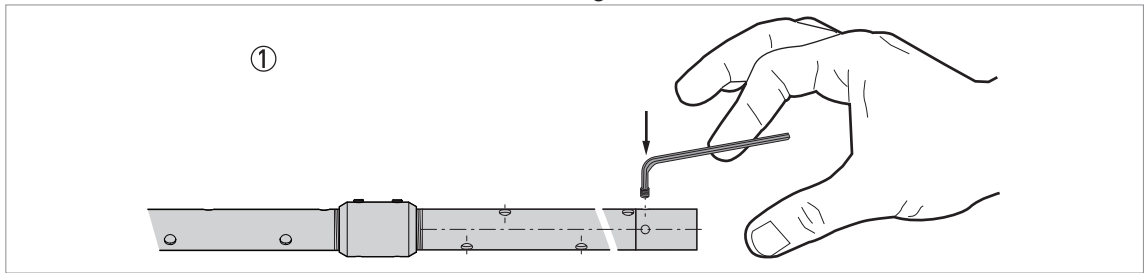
Parte 3: cómo ensamblar la sonda coaxial segmentada
